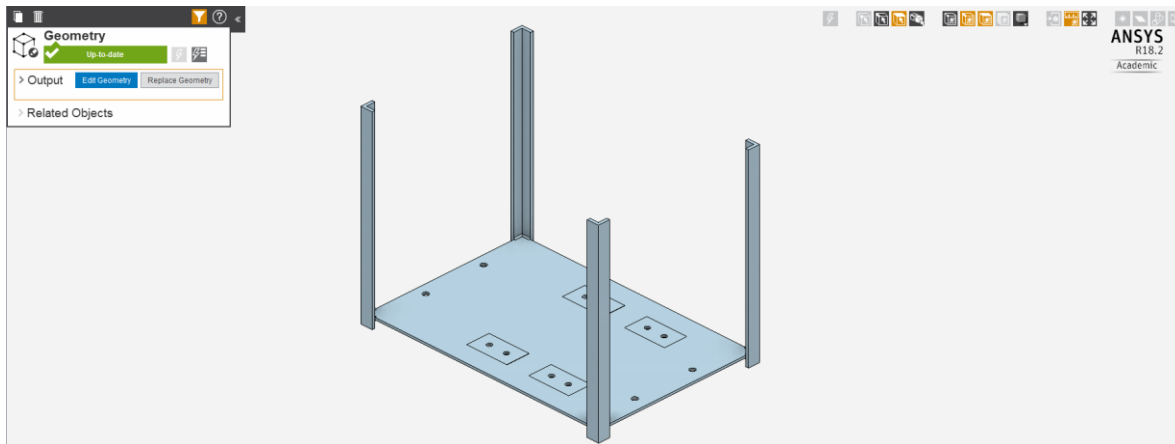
Modelado de la Placa Soporte del motor principal. Fuente Propia.
